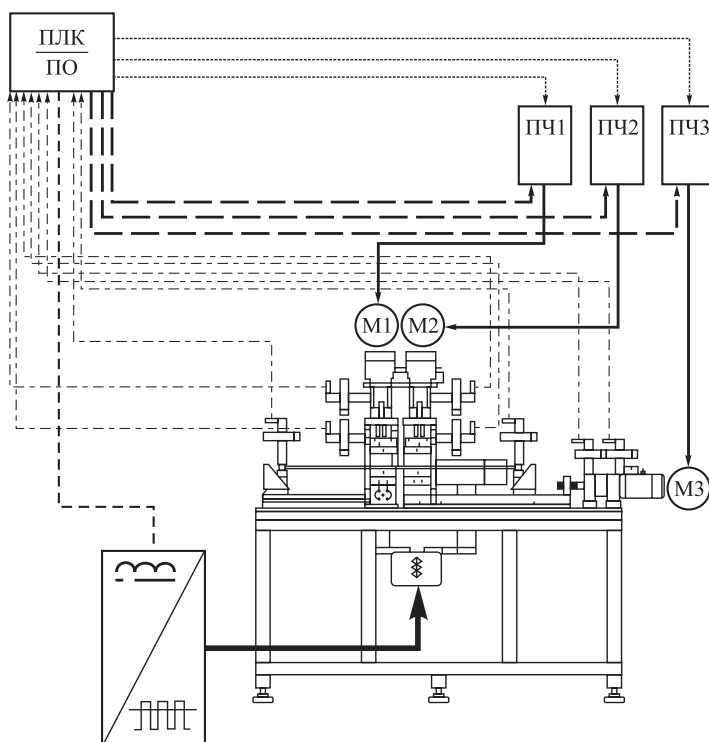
Система управления двухкоординатным станком сварки:
